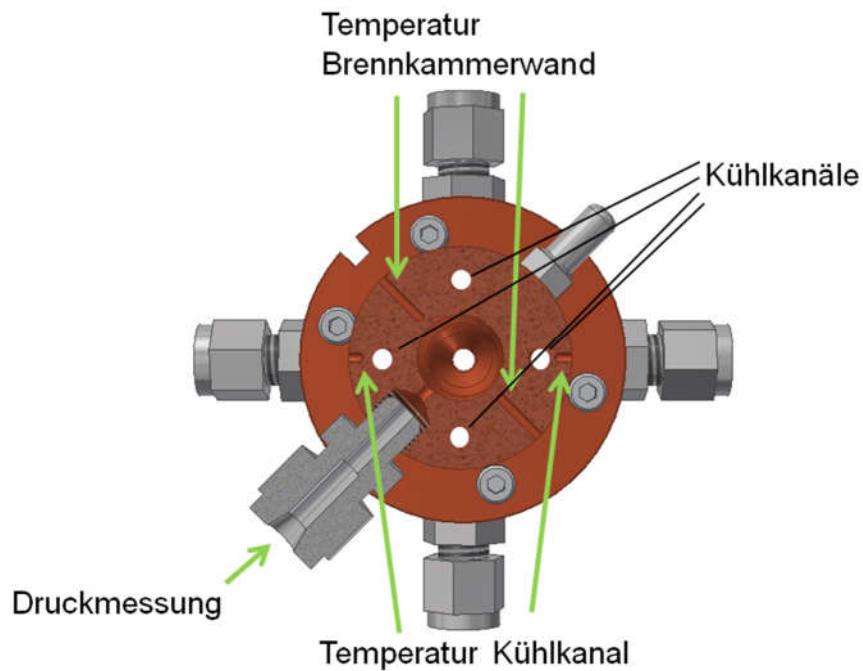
Brennkammer im Schnitt mit Kühlkanälen und Bohrungen für Thermoelemente
